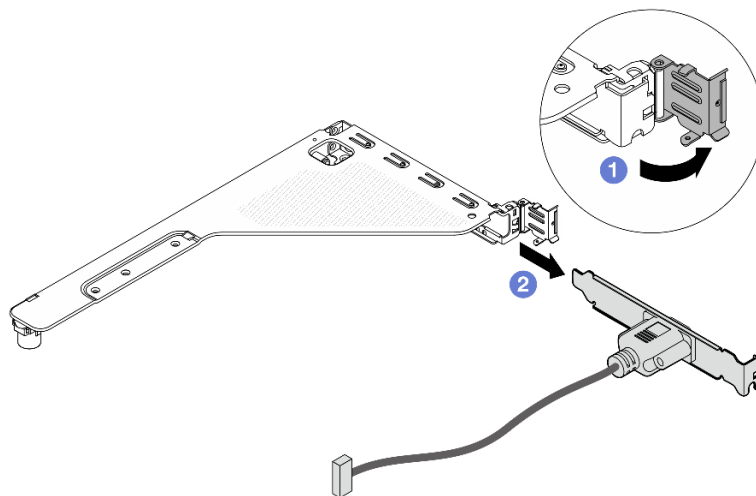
Entfernen des seriellen Anschlussmoduls
